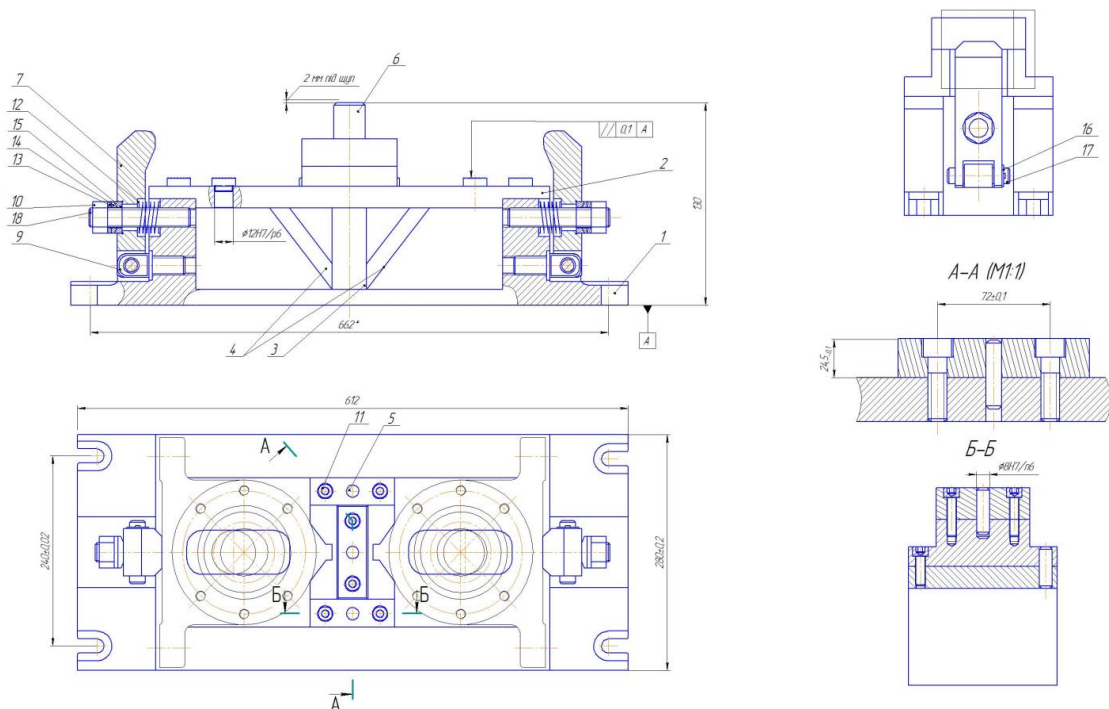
Схема пристрою для фрезерної, шліфувальної операції
